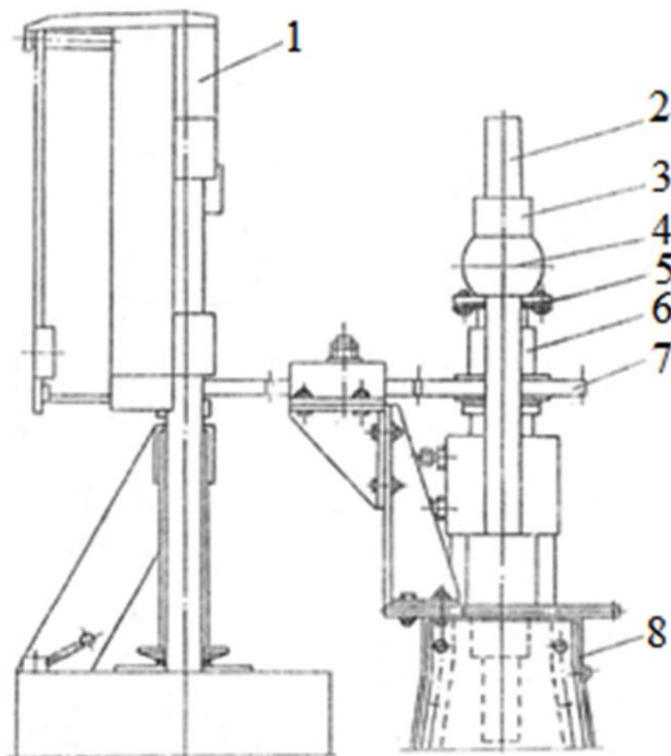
Общий вид установки для осуществления кручения под давлением 1-крутильная машина КМ-50; 2-колонна пресса; 3-гайка; 4- траверса пресса; 5-штулка поддерживающая блок наковален; 6-стакан, закрывающий блок наковален; 7- ведомая шестеренка главного узла установки, приводящая во вращение подвижные блоки наковальни; 8- станина пресса
